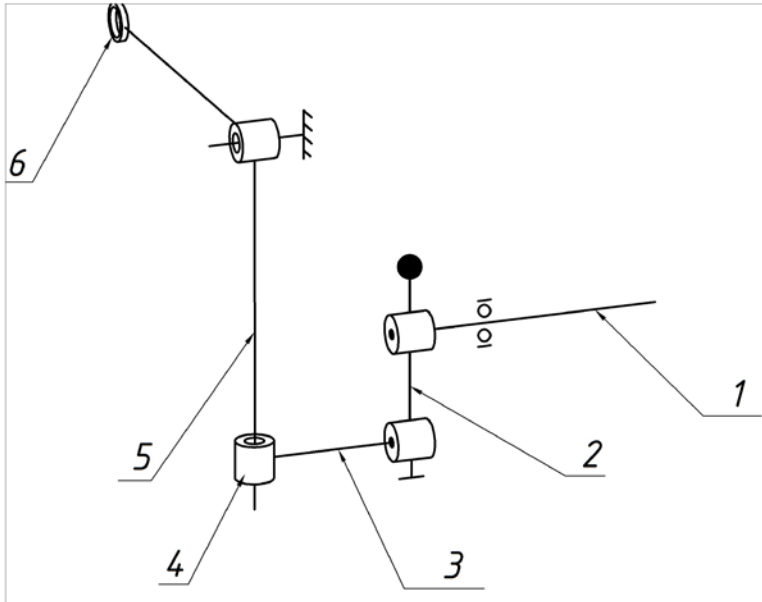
Механізм ниткопритягувача кулісного типу
